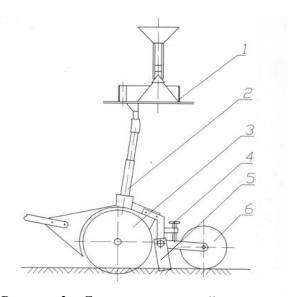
Схема высевающей секции экспериментальной самоходной селекционной сеялки: 1 — конический высевающий аппарат; 2 — семяпровод; 3 — дисковый сошник; 4 — регулировочный винт; 5 — загортачи; 6 — опорноприкатывающее колесо
